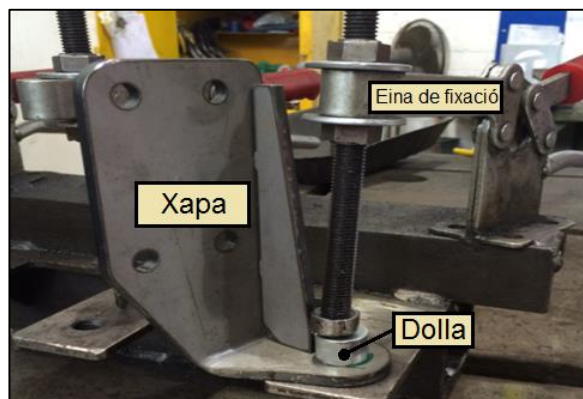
Fixació de l'adapter per a la soldadura manual.
